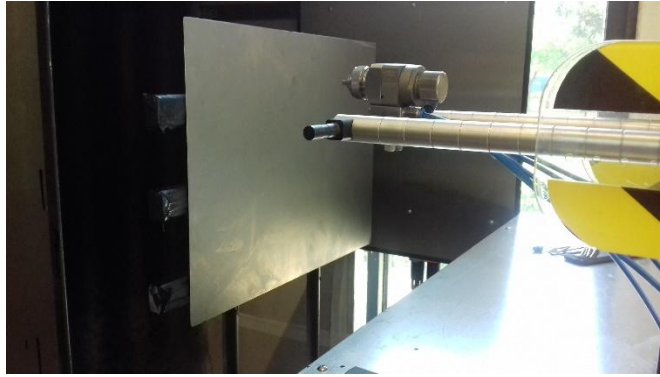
Base metálica para montaje de piezas plásticas para aplicación de pintura.
